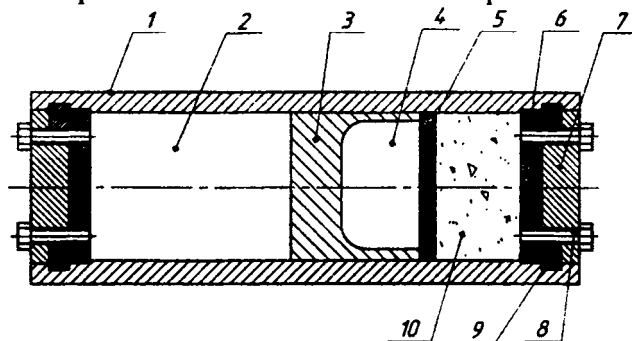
Модель конструкции взрывоударного контейнера с демпфирующей подушкой: 1 - цилиндр; 2 - ударная камера; 3 - поршень-ударник; 4 - взрывная камера; 5 - разделительная шайба; 6 - опорная крышка; 7 - стопорная крышка; 8 - болт; 9 - опорное полукольцо; 10- демпфирующая подушка.
